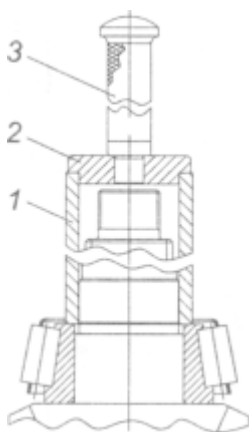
Запрессовка внутреннего кольца подшипника 32315В
